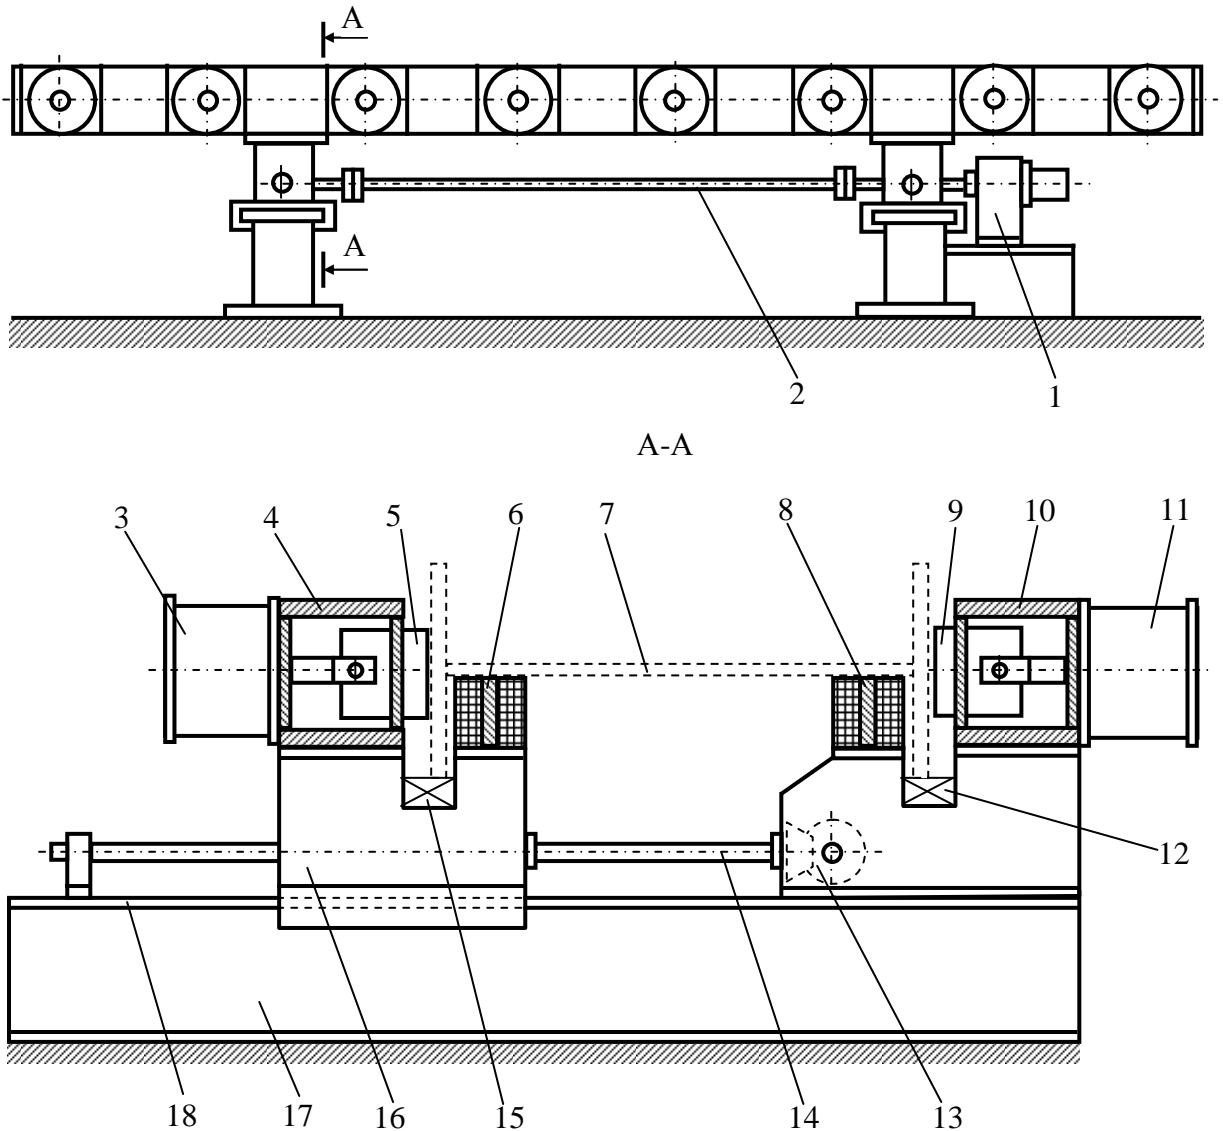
Стенд для складання та зварювання двотаврових балок без прихваток: 1-електропривод; 2-поздовжній вал; 3, 11-пневмоциліндри; 4- рухома опорна балка; 5, 9-притискачі; 6, 8-електромагніти; 7-двотавр, що складається; 10-нерухома опорна балка; 12, 15-зкладні сухарі; 13-конічна передача; 14-ходовий гвинт; 16-супорт; 17-фундаментна рама; 18- напрямна.
